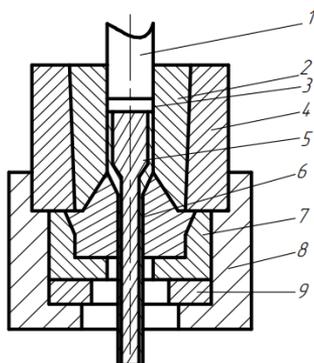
Схема прессования биметаллической заготовки «пруток»:
